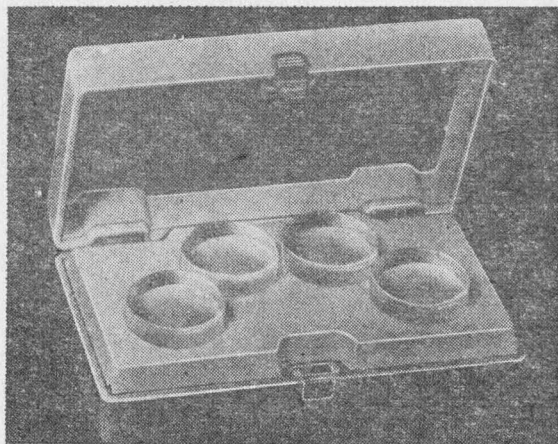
Trusă cu plăci de sticlă plan-paralele.
